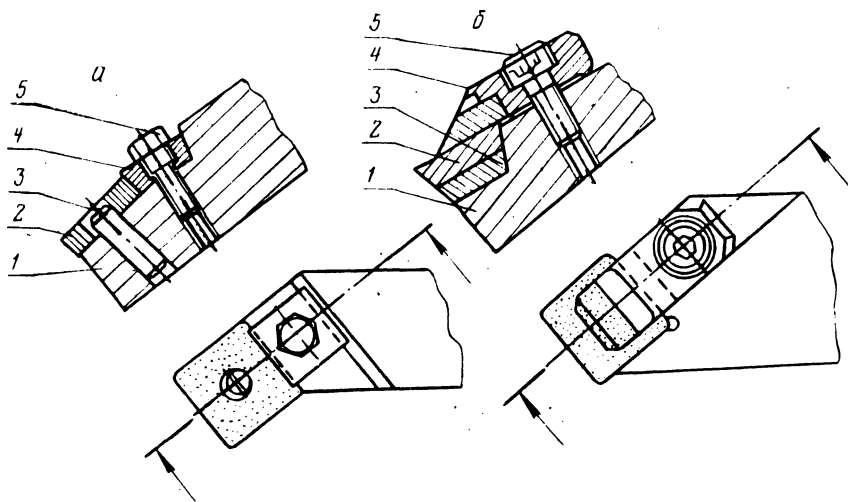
Сборные резцы разных конструкций: а – резец ВНИИ; б – резец фирмы Сандвик Коромант.
